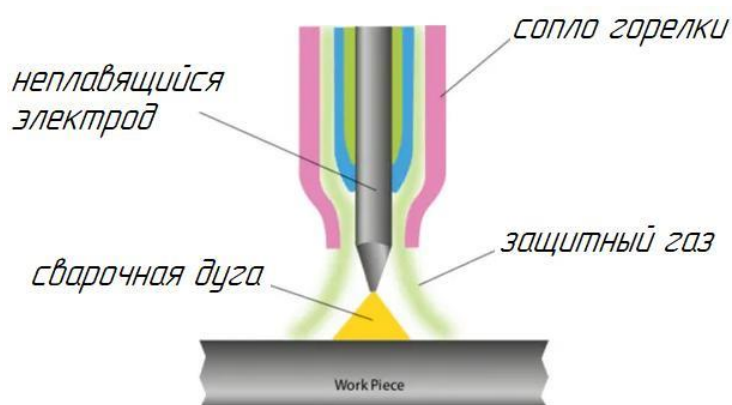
Схема аргонодуговой сварки неплавящимся электродом
